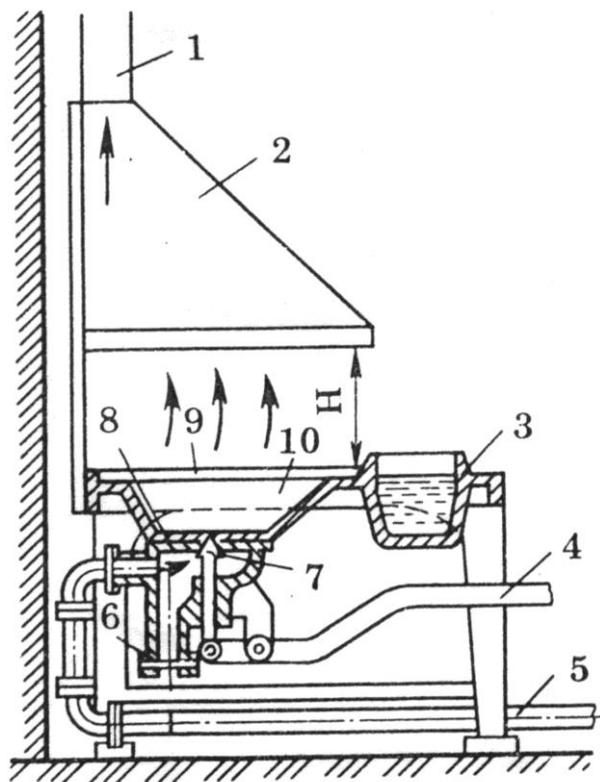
Оборудование для нагрева заготовок: 1 – вытяжная труба; 2 – зонт;
